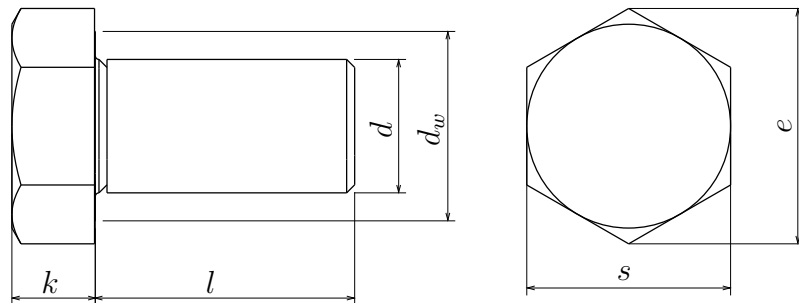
Befestigungsschraube nach DIN EN ISO 4017 mit Regelgewinde bis zum Kopf
